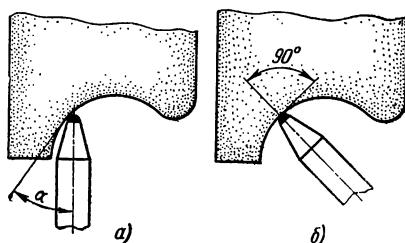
Схема установки алмаза при профилировании шлифовального круга
